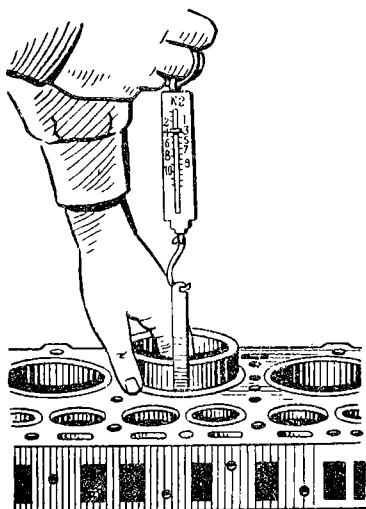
Проверка зазора между юбкой поршня и цилиндром
